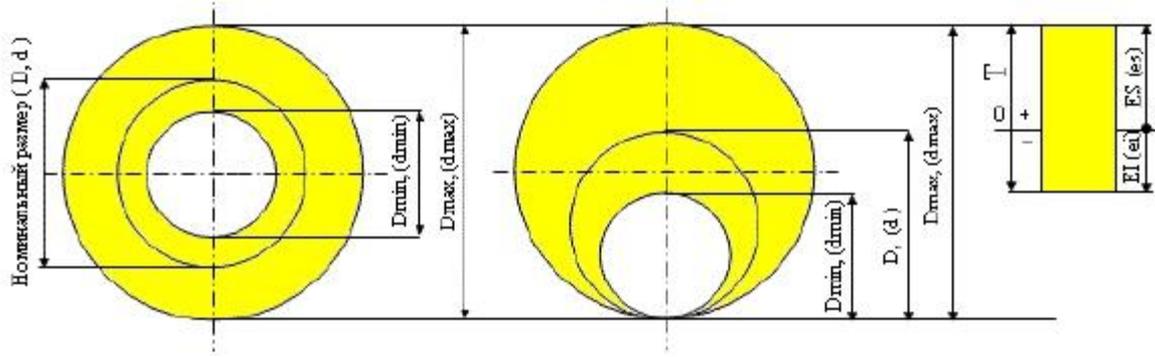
Поле допуска (T) для общего случая
